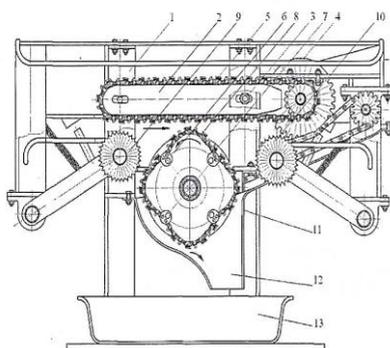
Устройство для заготовки хвойной лапки (вид сбоку)
